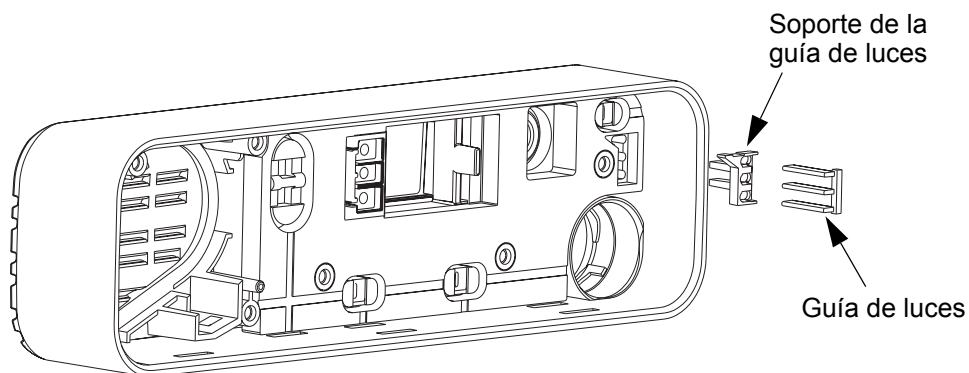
Montaje de la guía de luces y el soporte de la guía de luces
